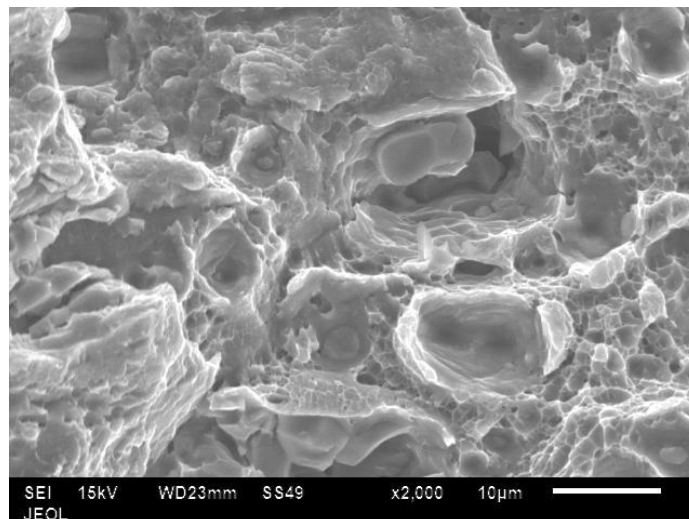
Analyse fractographique à 20 mm de l'entaille pour une éprouvette réparée sous L-H blocs à 1x 100
